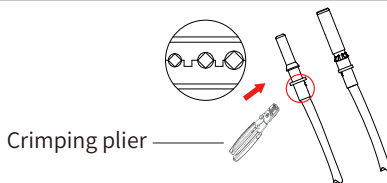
Crimpen des Kontaktstifts an den Draht
